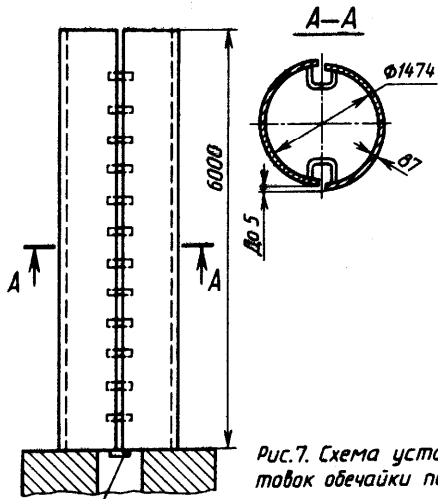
Схема установки заготовок обечайки под сварку
